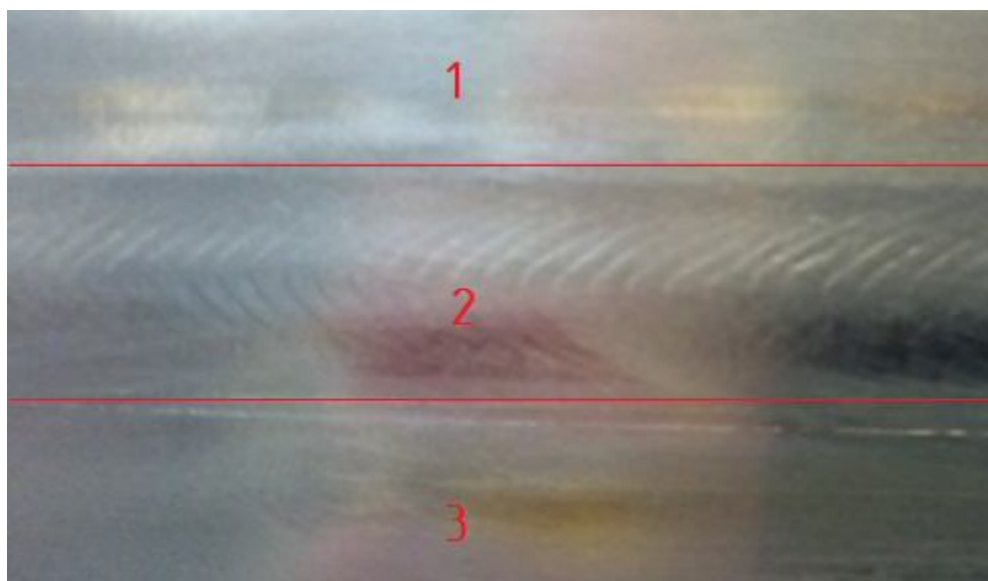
Внешний вид исследуемого сварного соединения: участки 1 – обечайка; 2 – сварной шов; 3 – силовой элемент
